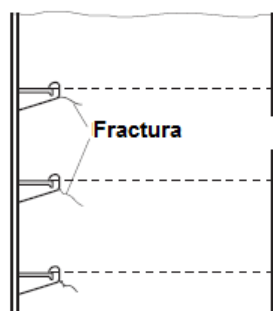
Aperturas para el paso de refuerzos a través de los mamparos
